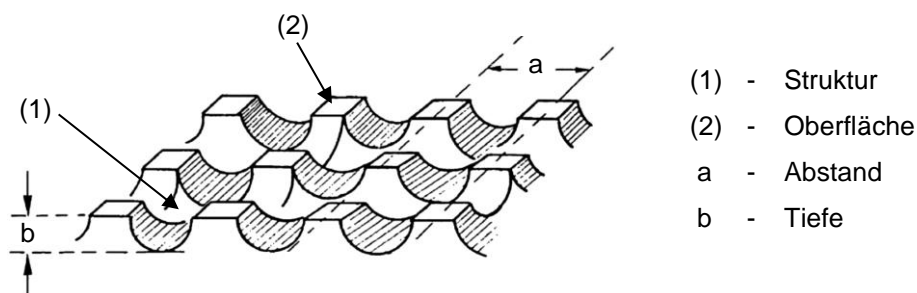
Patentierte Oberflächenstruktur für das Stranggießen [121; 122]
